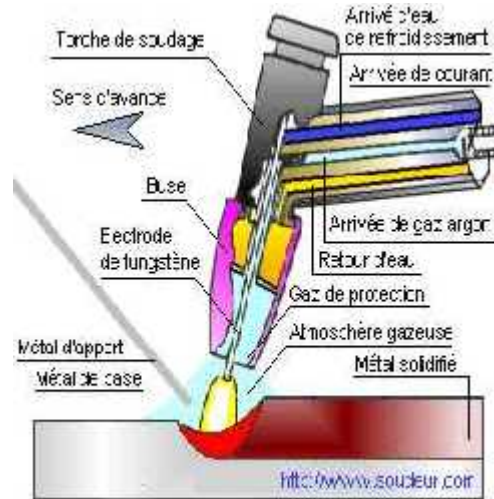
b : Principe de la soudure "TIG"
